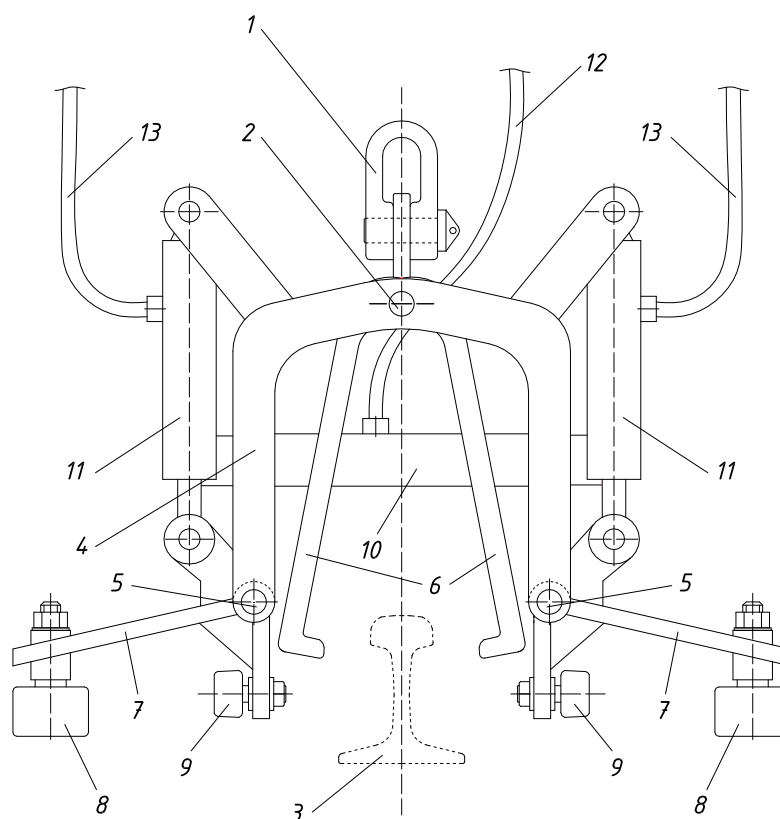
Главный вид двойного роликового рельсового захвата в транспортном положении
